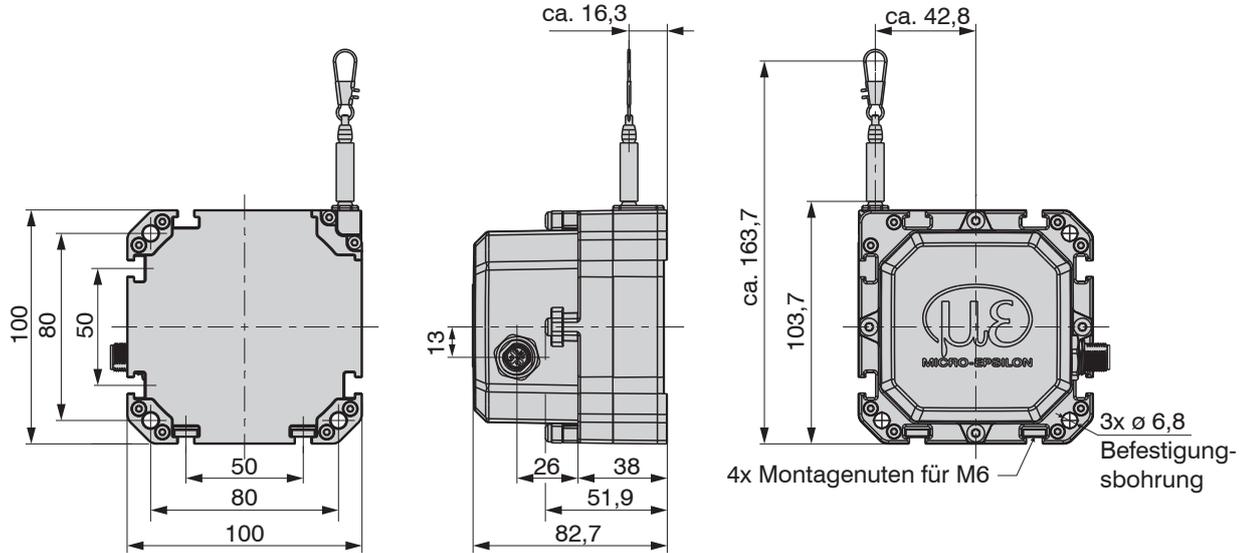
Maßzeichnung WPS-1500-K100, WPS-2500-K100 mit Steckverbinder 5-polig M12x1, Abmessungen in mm
